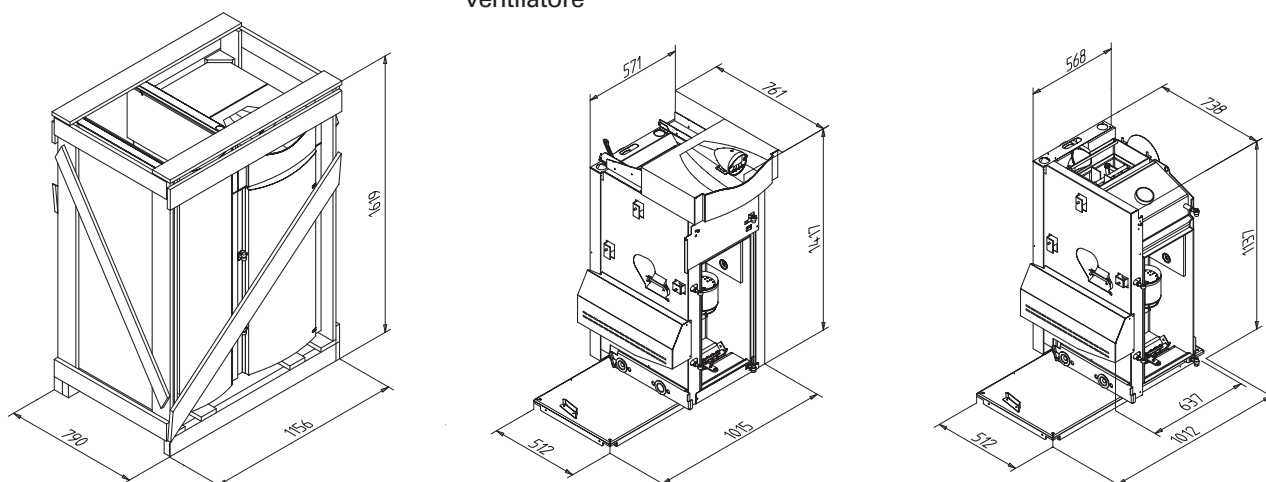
Caldaia a pellets BioWIN - Smontaggio di parti componenti
